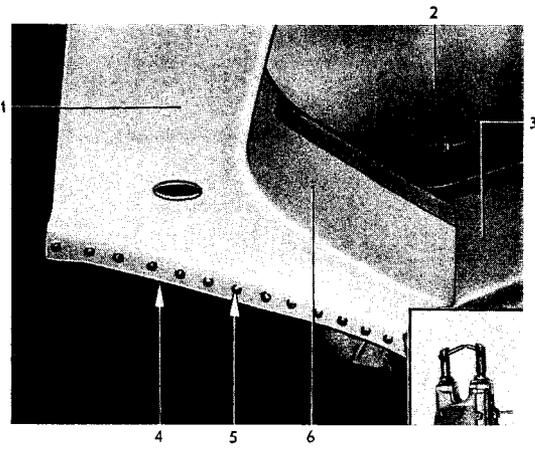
Unterer waagerechter Flansch der rechten Seitenstrebe punktgeschweißt – Linke Seitenstrebe in gleicher Weise punktschweißen
